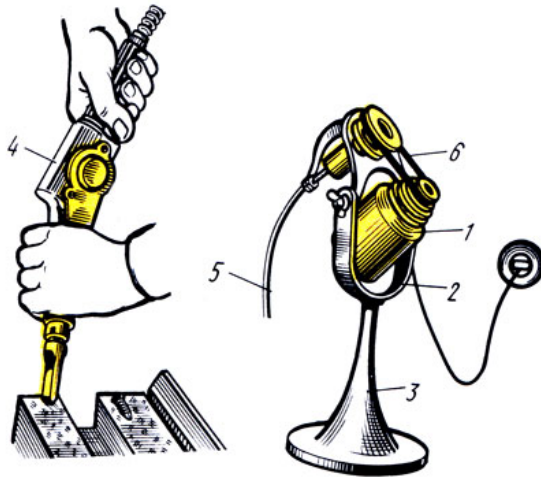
Стационарная шабровочная головка: 1 - электродвигатель, 2 - кронштейн, 3 - станина, 4 - головка, 5 - гибкий вал, 6 - клиноременная передача
